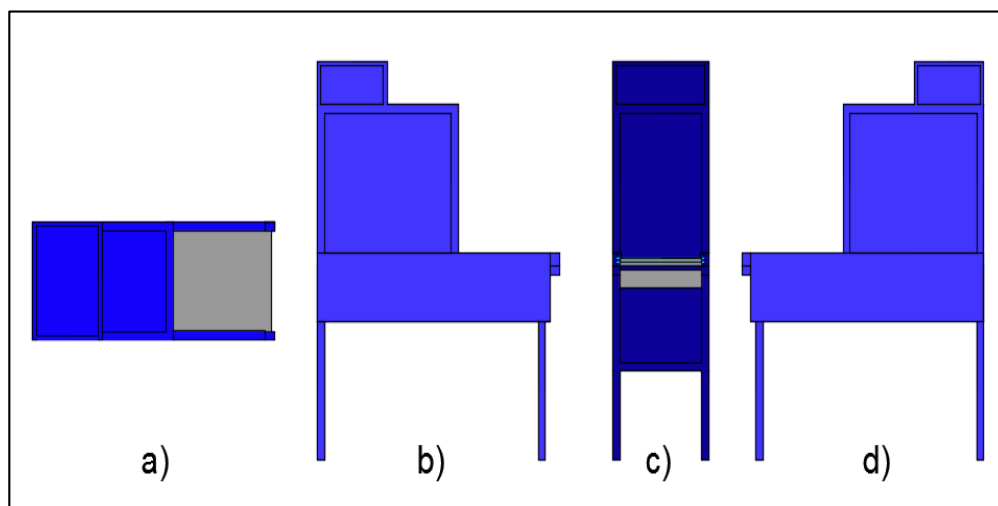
Proyección ortogonal de la cabina estructural. a) Vista superior/ planta, b) Vista de perfil derecho, c) Vista frontal/alzado, d) Vista de perfil izquierdo
